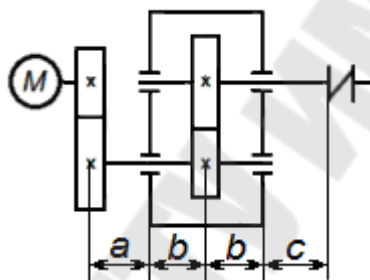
Кинематическая схема привода с открытой цилиндрической зубчатой передачей
